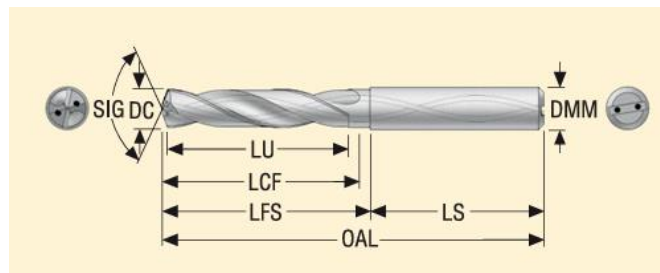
Свердло SD1103A-0675-024-08R1; покриття TiAlN [5, с. 32]
